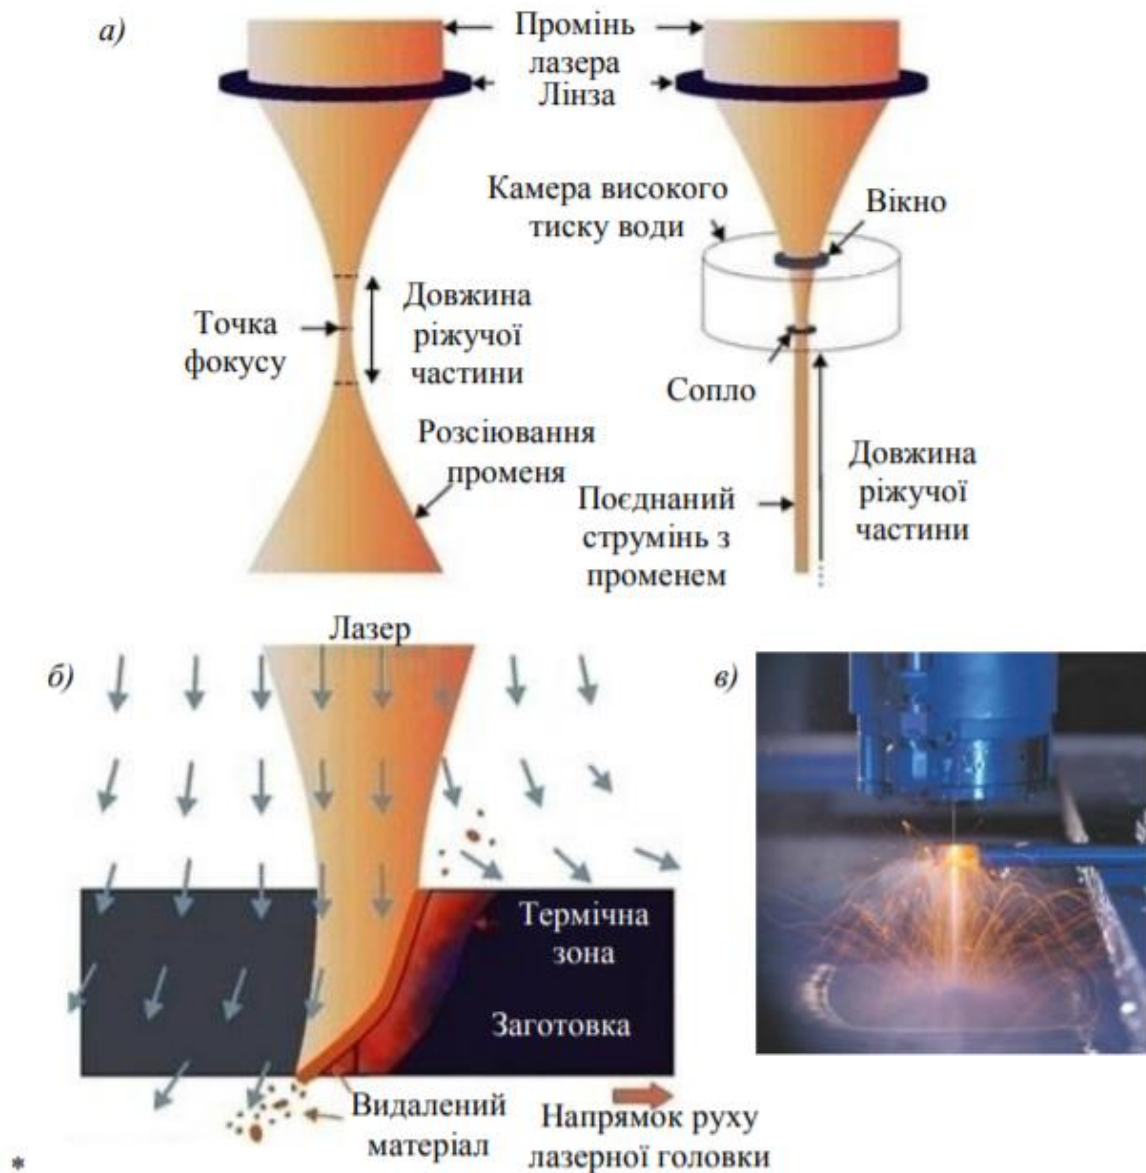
Формування струминно-лазерного потоку, з його подальшим впливом на оброблювану поверхню [25]; а) – формування струминно-лазерного потоку; б) – вплив потоку на заготовку в зоні різання; в) – різання листової заготовки.
